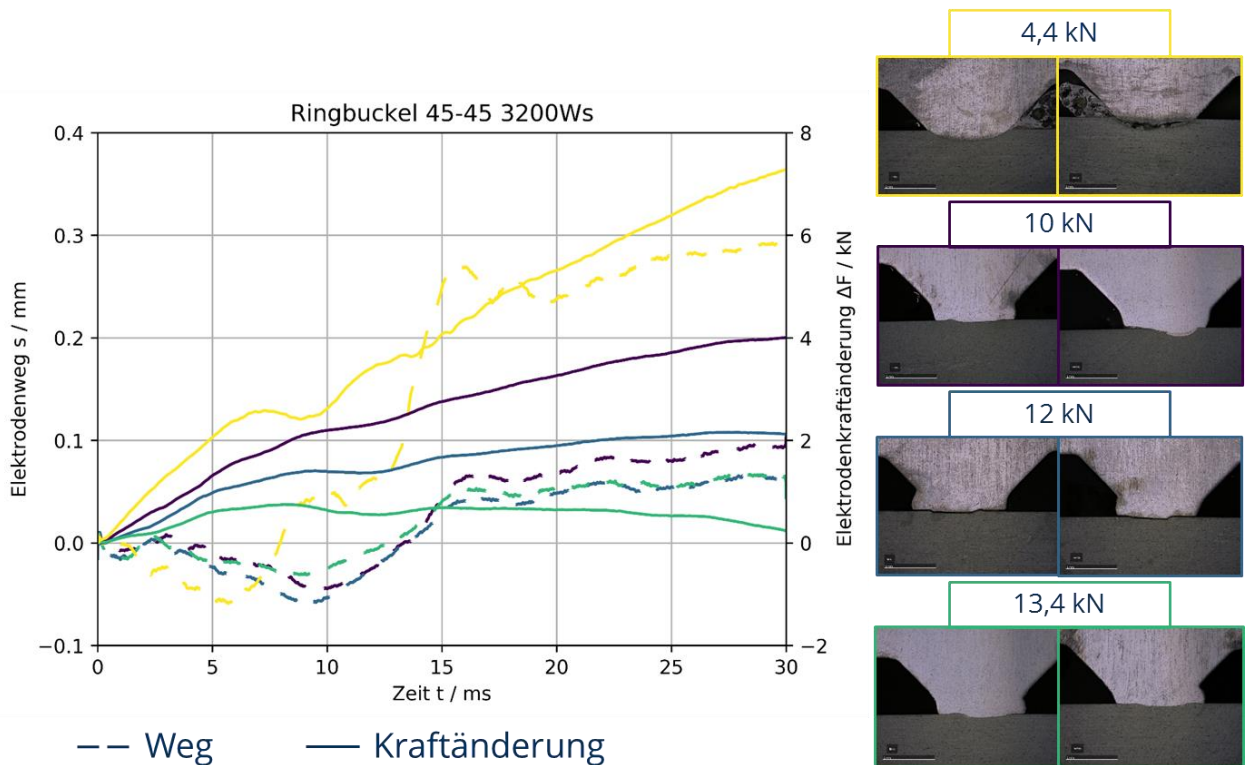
Weg- und Kraftänderung an Maschine 1- Ringbuckel mit Flankenwinkeln 45°/45°
